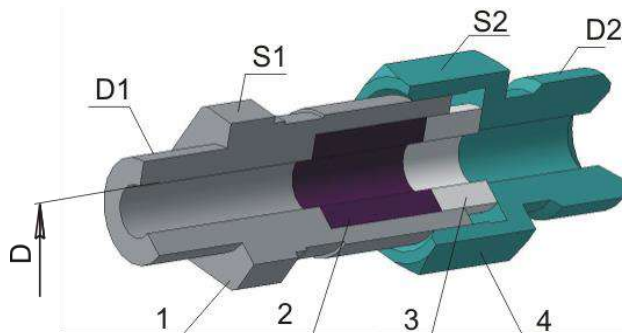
Конструкция кабельного ввода для монтажа кабеля в трубе
